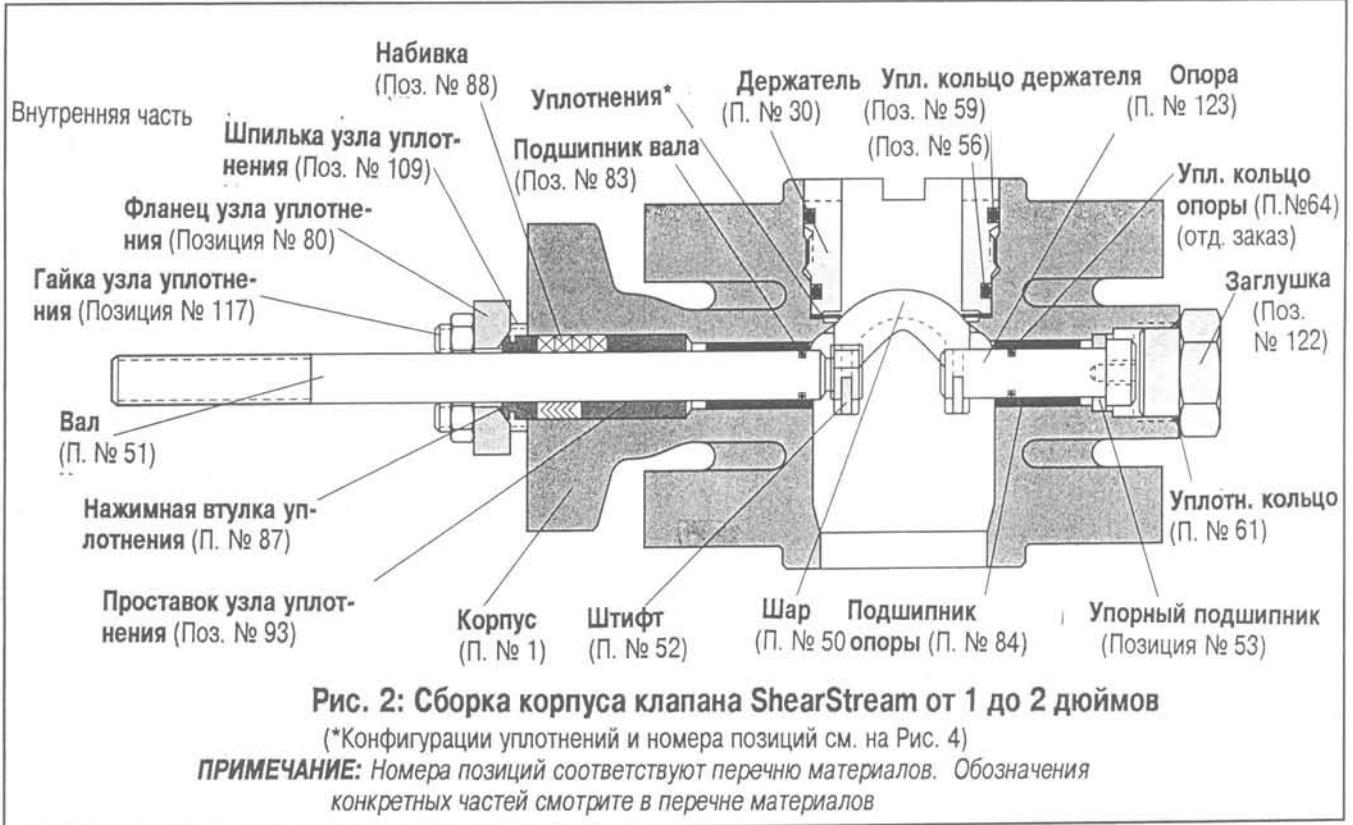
Сборка корпуса клапана ShearStream от 1 до 2 дюймов
